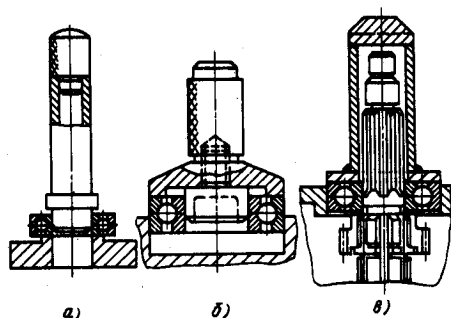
Схемы установки подшипников качения на валы и в корпуса с использованием оправок
